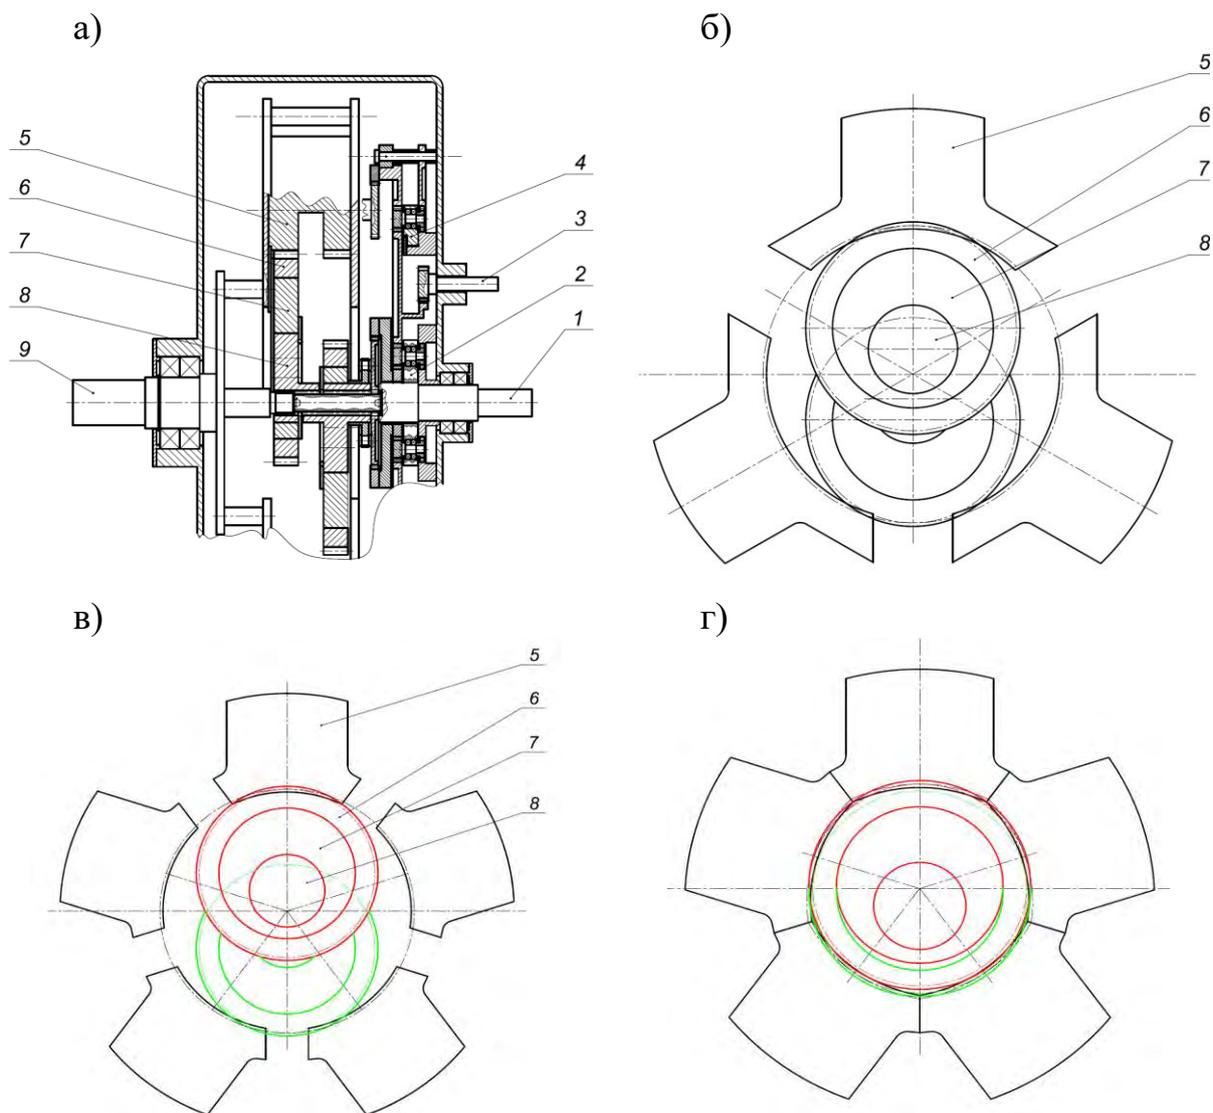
Компонка планетарной плавнорегулируемой передачи по схеме 2: а – принцип действия передачи; б – схема расположения секторов центрального зубчатого колеса; в – пятисекторное центральное зубчатое колесо при минимальном передаточном отношении передачи; г – пятисекторное центральное зубчатое колесо при максимальном передаточном отношении передачи
